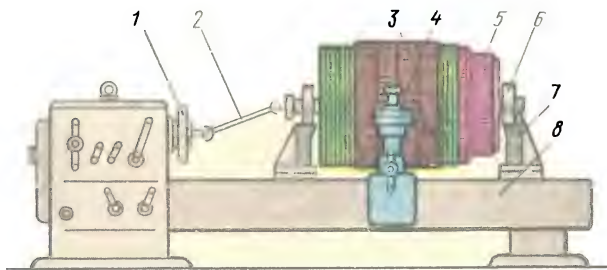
Якорь, установленный на токарно-винторезном станке для проточки коллектора
